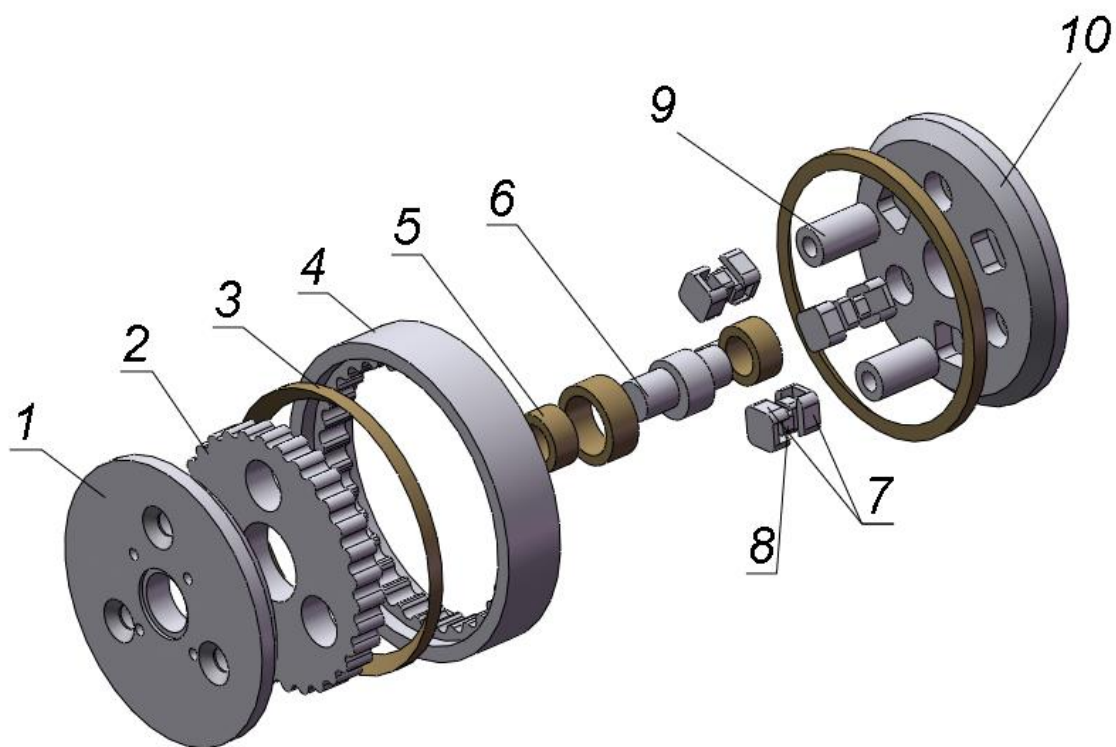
Разнесенный вид волнового кинематического редуктора. 1 – корпус; 2 – шестерня; 3 – подшипник; 4 – зубчатое колесо; 5 – втулка; 6 – вал-эксцентрик; 7 – направляющие; 8 – крепеж; 9 – втулка распорная; 10 – корпус.
